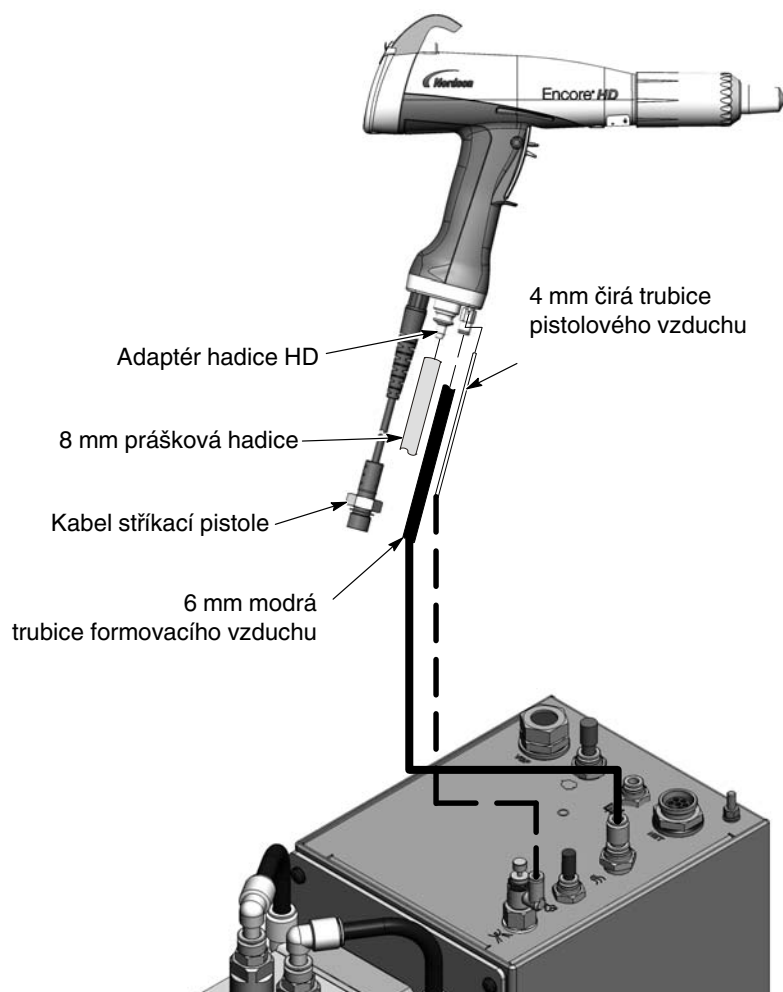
Připojení kabelu stříkáč pistolí k řídicí jednotce systému – zobrazen mobilní systém
